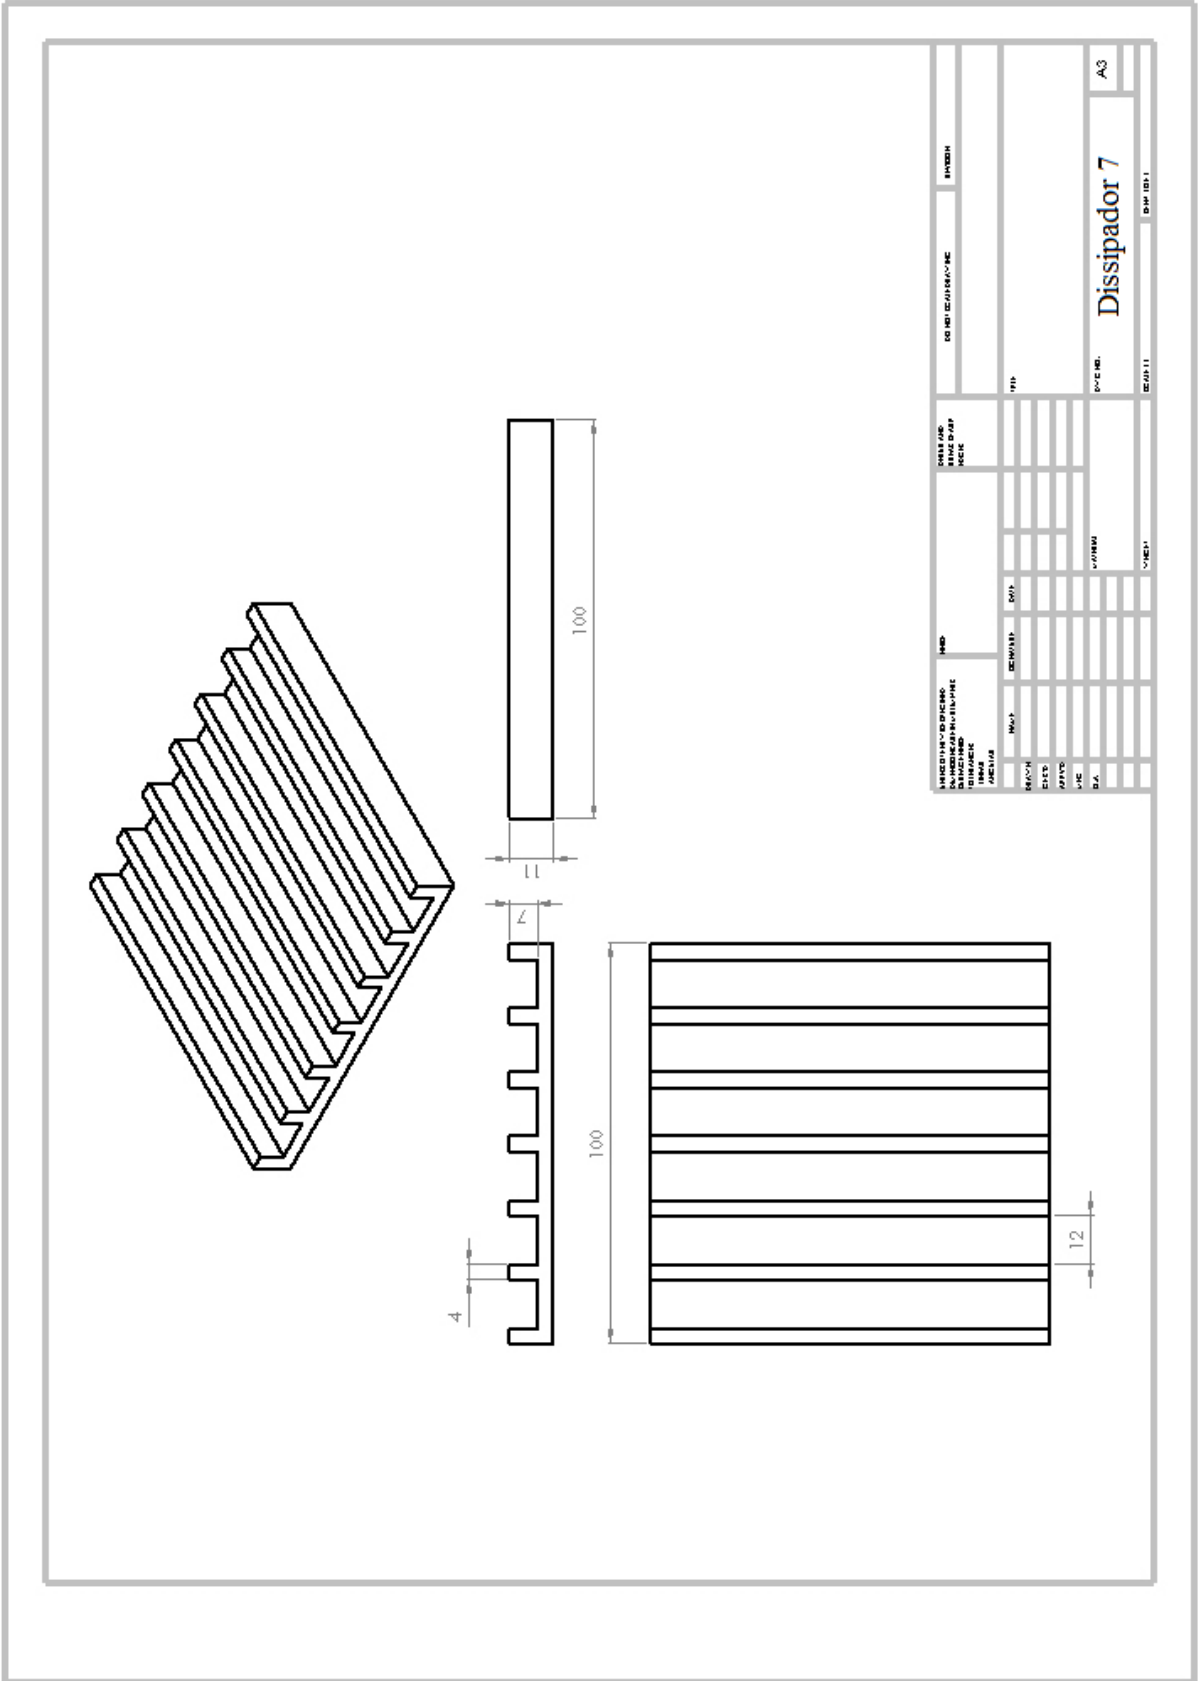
Desenho técnico utilizado para confecção do Dissipador 7.
